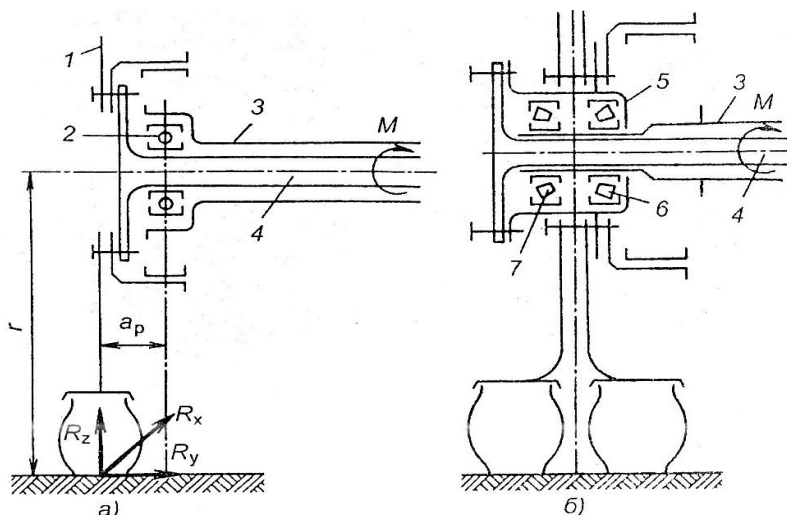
Кинематические схемы внешней опоры полуосей: а – полуразгруженной; б – разгруженной; 1 – диск колеса; 2,6,7 – подшипники; 3 – кожух; 4 – полуось; 5 – ступица
